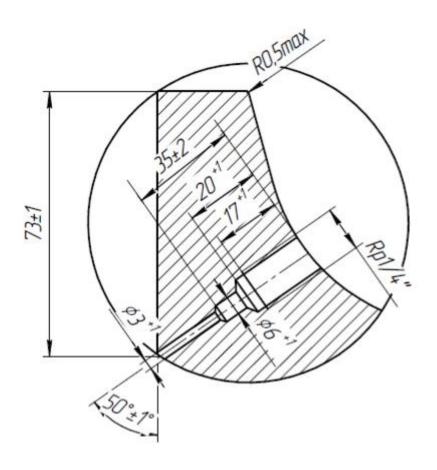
Масленочное отверстие колеса Ø 750 мм (ссылочный № 29240, ред. Е)
